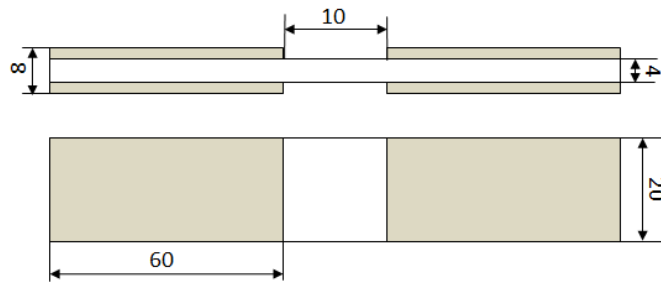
Dimensions des éprouvettes de compression à 0°
